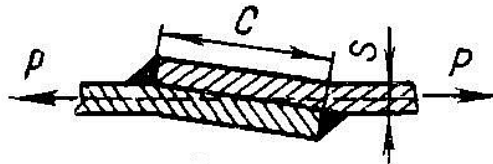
З'єднання з двома розрахунковими лобовими швами
